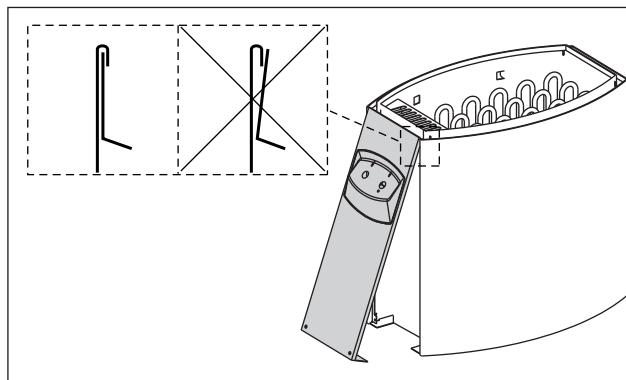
Fermeture du couvercle du boîtier de connexion (toutes les dimensions sont fournies en millimètres)
